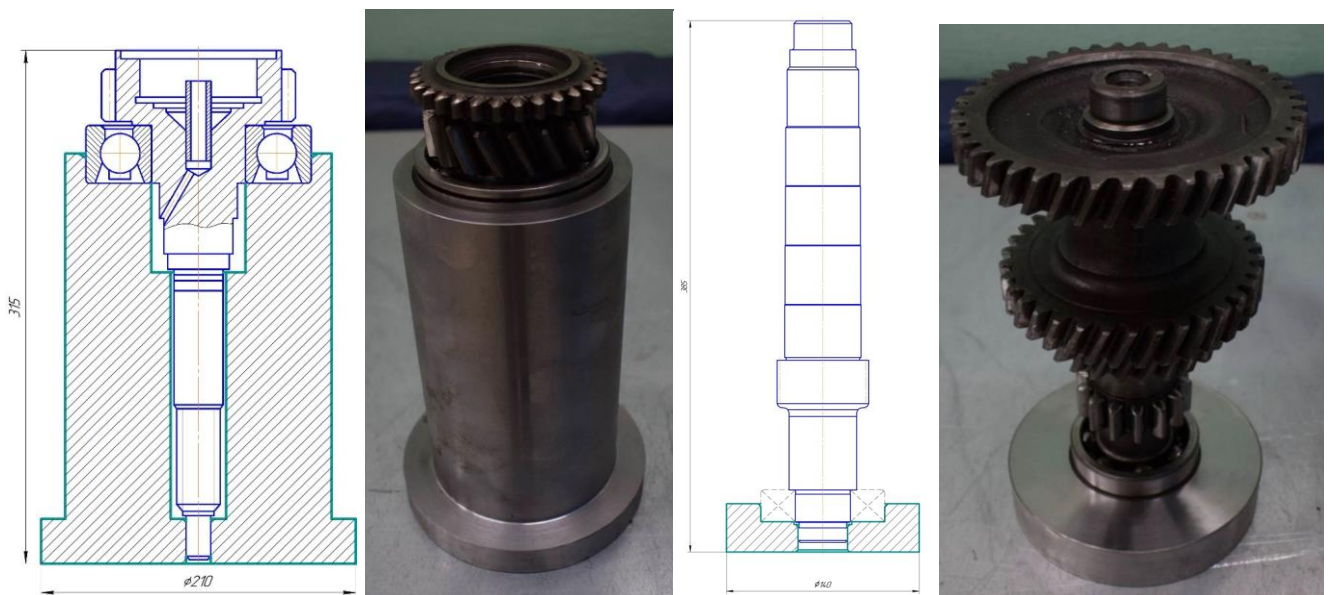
Центрирующие приспособления для клеевых соединений типа «вал-подшипник»
